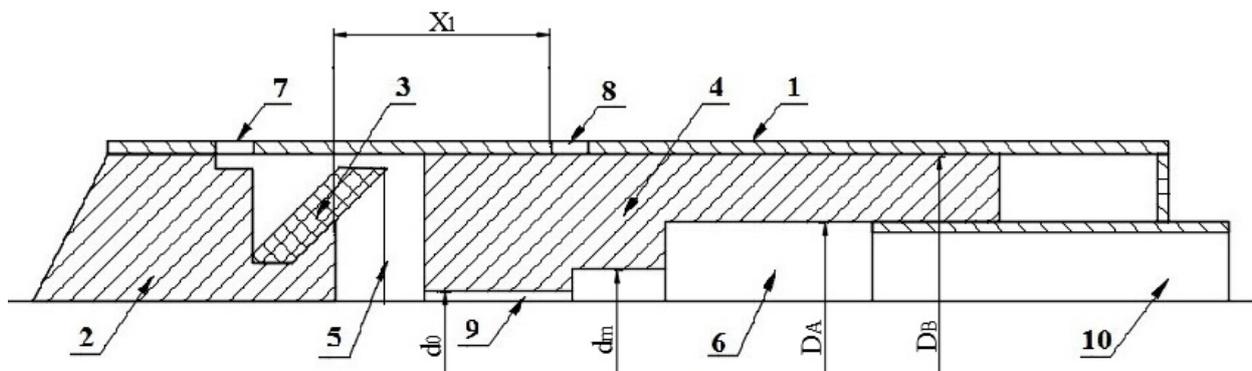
Принципиальная схема ударной машины: 1 — корпус; 2 — наковальня; 3 — клапан; 4 — боек; 5 — камера обратного хода; 6 — камера прямого хода; 7 — первое выхлопное отверстие; 8 — второе выхлопное отверстие; 9 — межкамерный дроссель; 10 — подача воздуха
